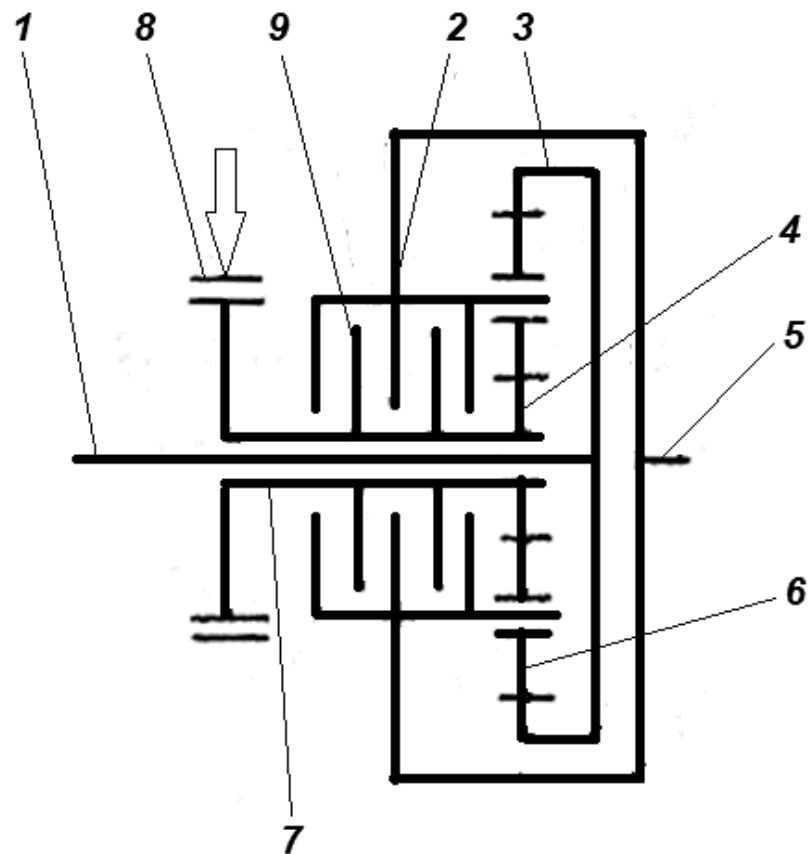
Принципова схема ЗКМ на базі планетарного редуктора [88]:
